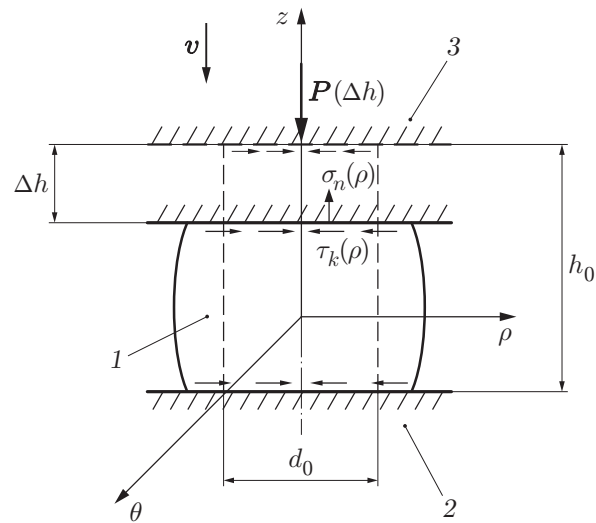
Схема осадки цилиндрической заготовки плоскими бойками: штриховые линии — исходное состояние заготовки; сплошные — текущее; 1 — заготовка; 2 — неподвижный боек; 3 — подвижный боек
